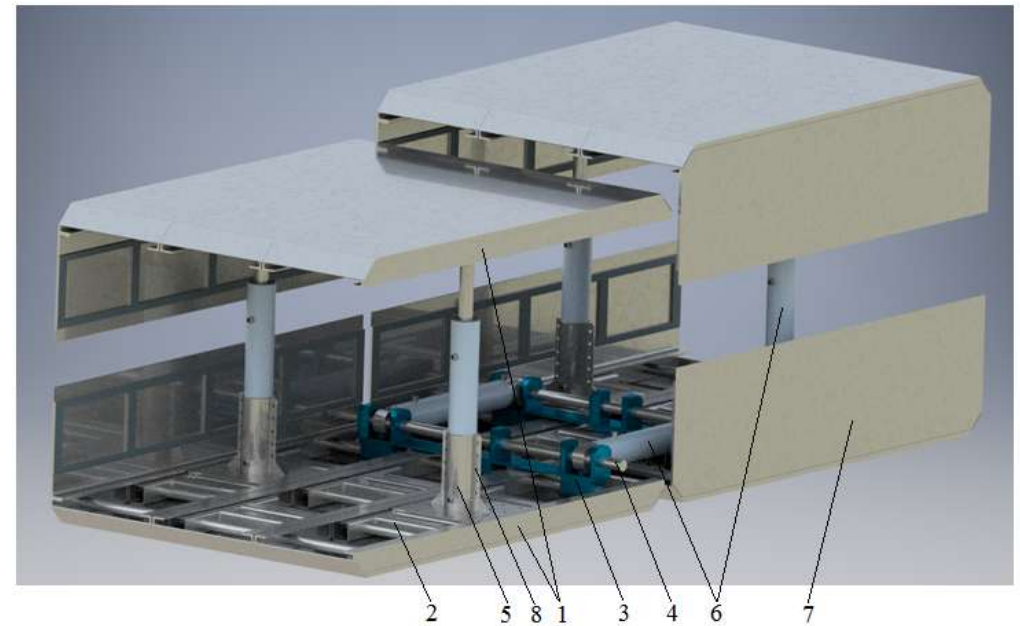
Конструкция шагающей крепи проходческого комплекса: 1 – перекрытия крепи; 2 – основание; 3 – упор гидродомкрата; 4 – стержень; 5 – упор гидростойки; 6 – гидростойка (гидродомкрат); 7 – ограждения крепи; 8 – крепежные элементы
